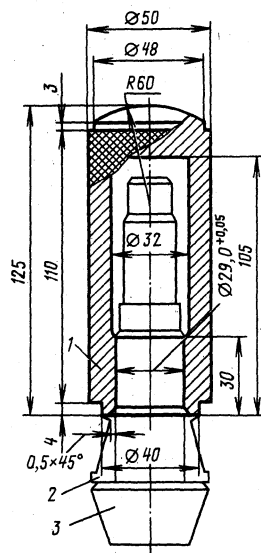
Оправка для напрессовки внутреннего кольца заднего подшипника на вал ведущей шестерни главной передачи автомобиля «Москвич»:
